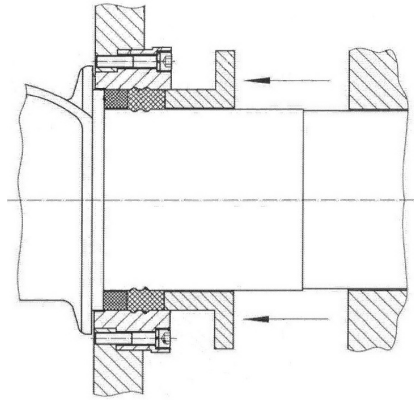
Контактний ущільнювальний пристрій сальникового типу згідно з пат. № CN203566878U
